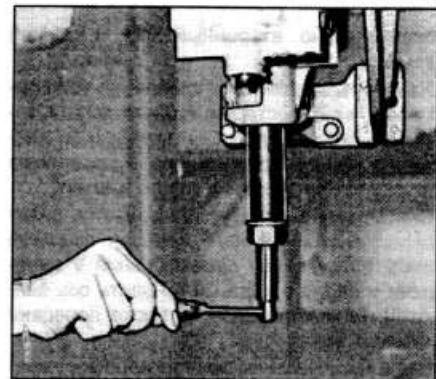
Установка вторичного вала в заднюю крышку коробки передач с помощью приспособления 16.042
